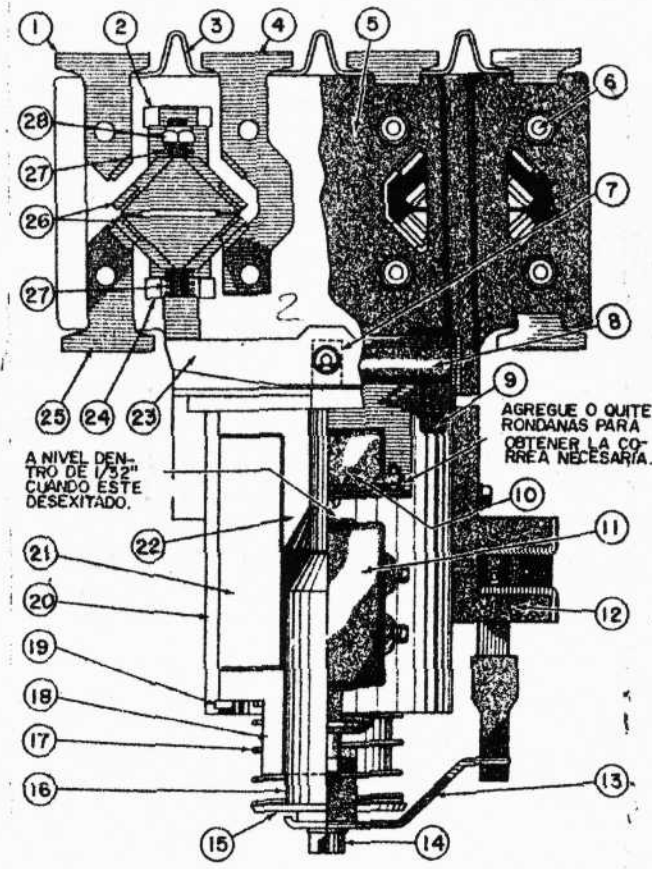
CORTE SECCIONADO DE EL CONTACTO 8251586
